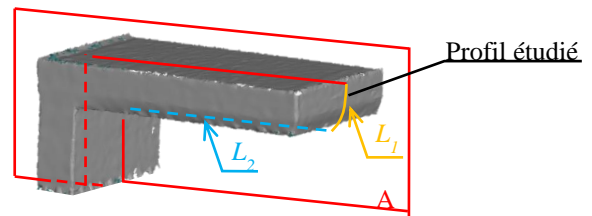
CONSTRUCTION DU PROFIL POUR CHAQUE PIECE.
